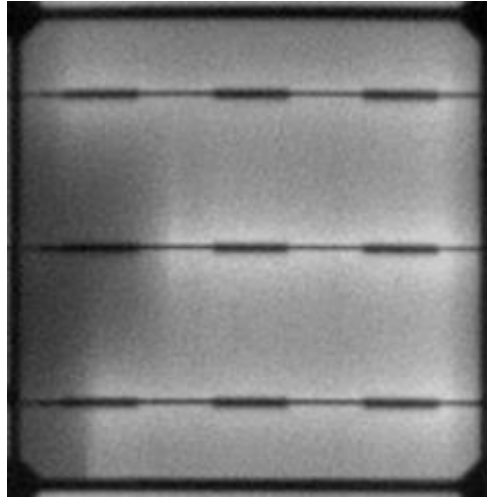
Fotografía de una célula afectada por defecto de soldadura en cinta. (PV-Elaboración Propia, 2020)
